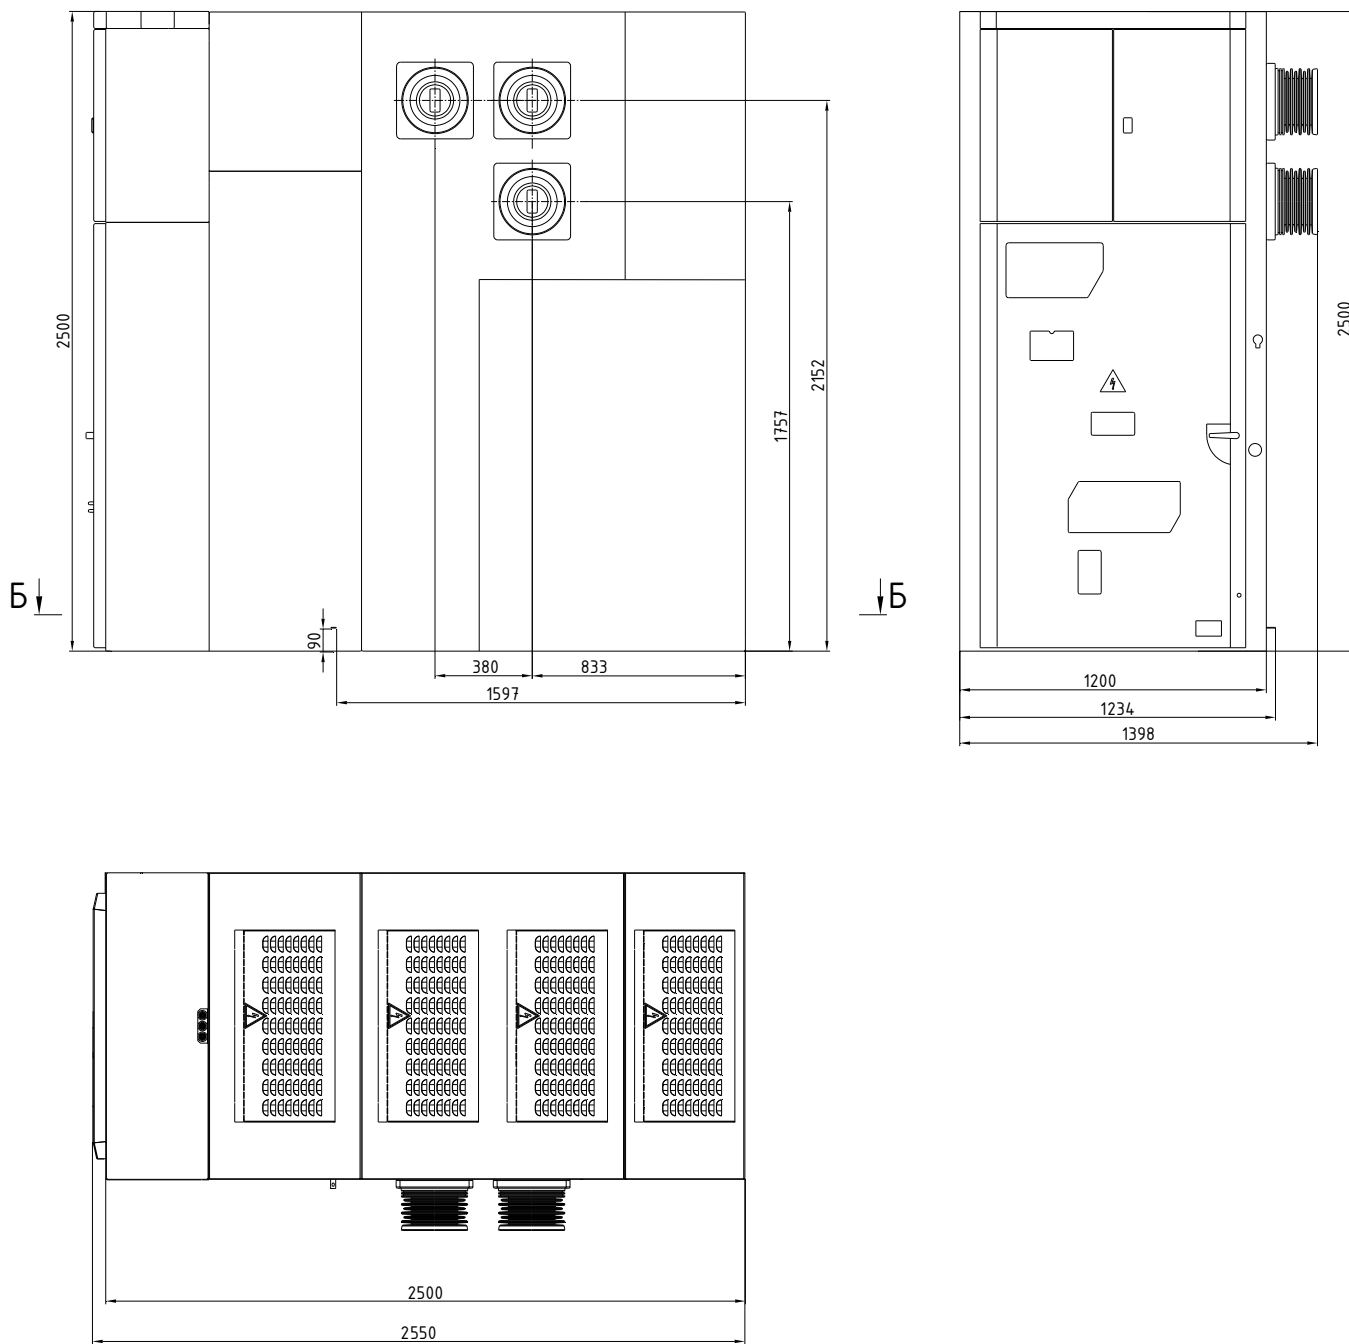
Габаритные размеры шкафов КРУ с верхним расположением сборных шин
